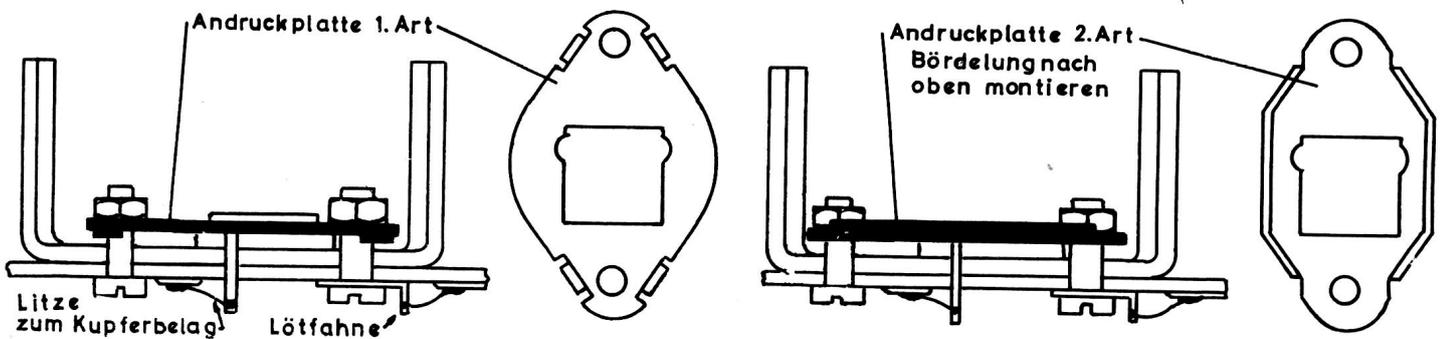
Befestigung der Transistoren E 11 und Kühlkörper
